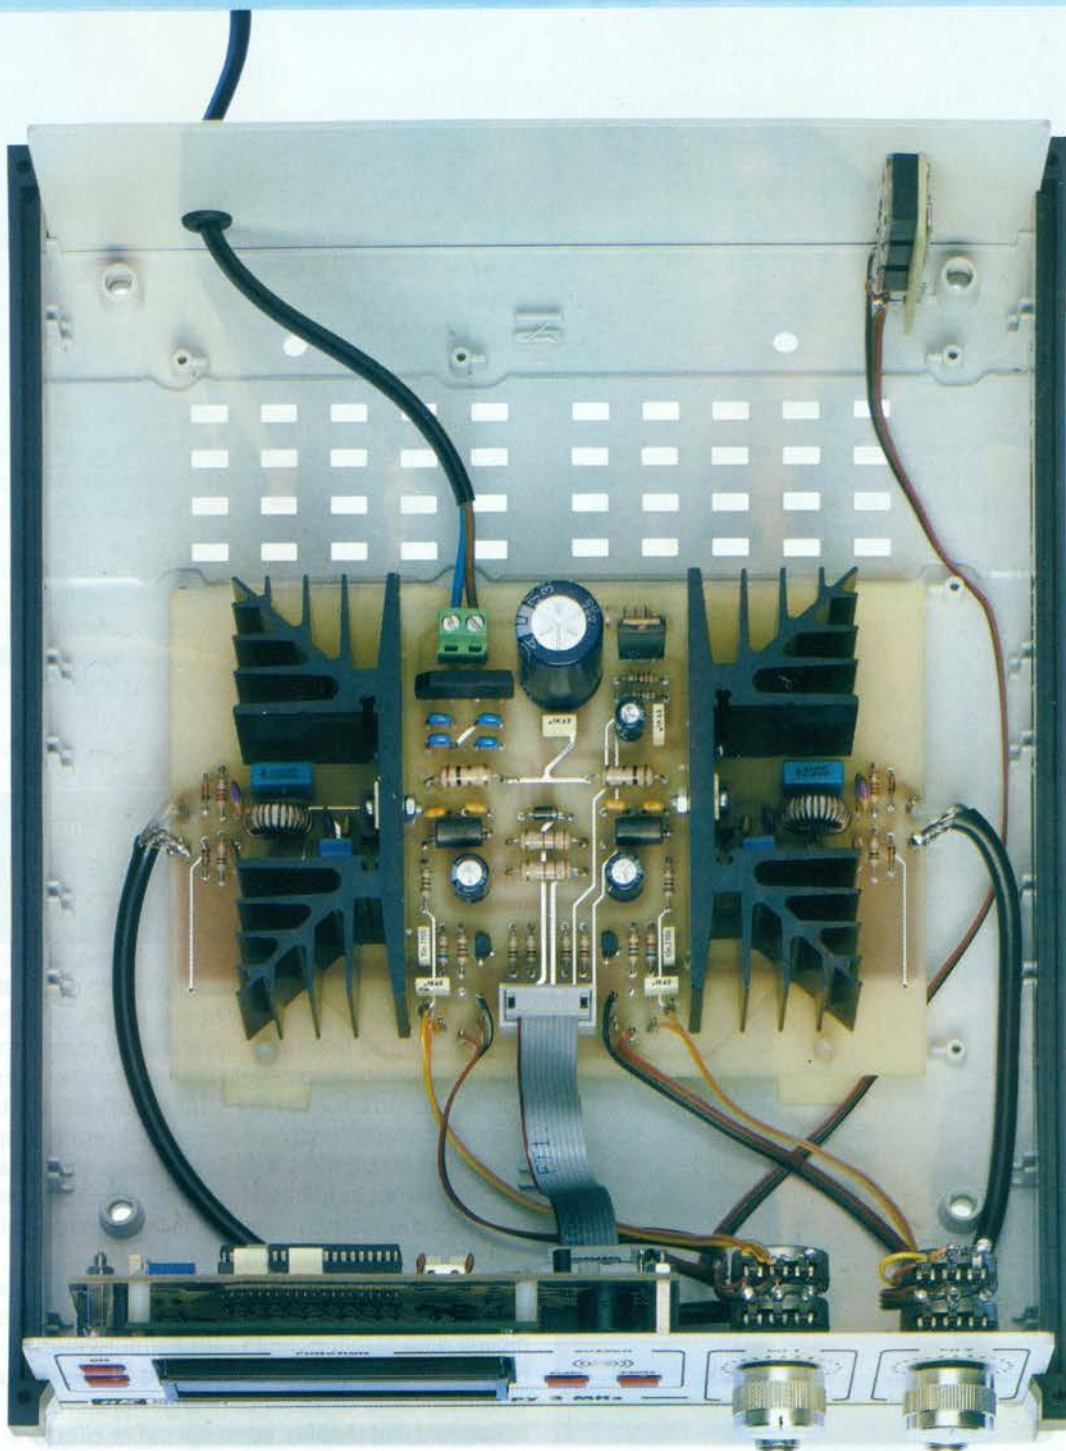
In questa foto è ben visibile il cablaggio dei cavetti di collegamento tra il circuito stampato LX.1660 fissato sulla base del mobile, il circuito stampato del display LX.1661 e quello dei Jack LX.1661/B fissati rispettivamente sulla mascherina frontale e sulla mascherina posteriore del mobile.
